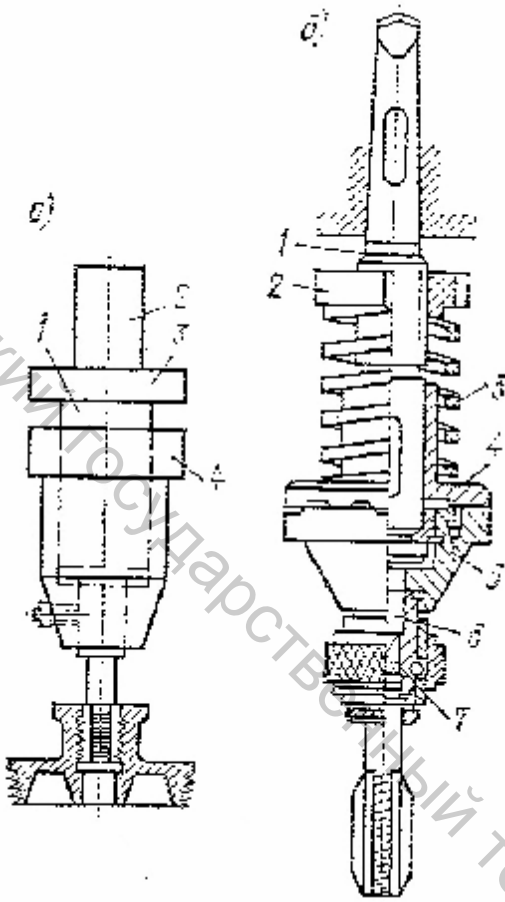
Самовыключающиеся патроны для нарезания резьб метчиками
